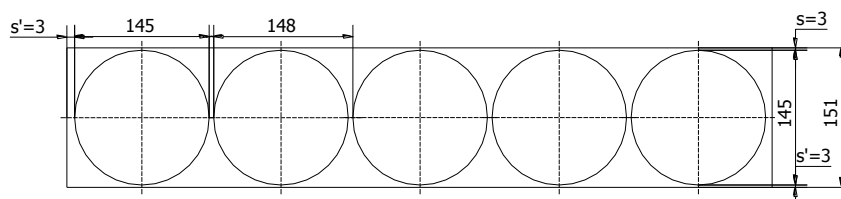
Disposición normal de la pieza con la plancha en sentido horizontal.
